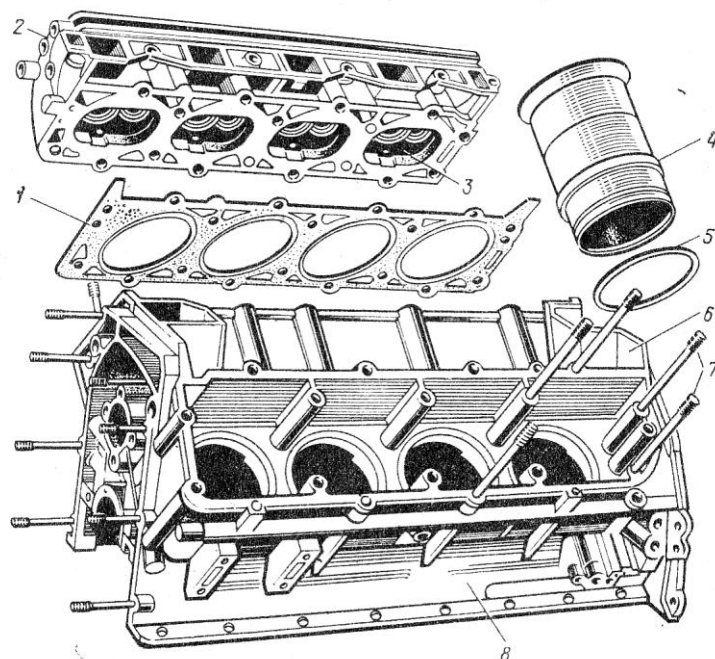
Неподвижные элементы кривошипно-шатунного механизма V-образного двигателя: 1 – прокладка; 2 – головка цилиндров; 3 – камера сгорания; 4 – гильза; 5 – уплотнительное кольцо; 6 – блок цилиндров; 7 – шпильки; 8 – картер
